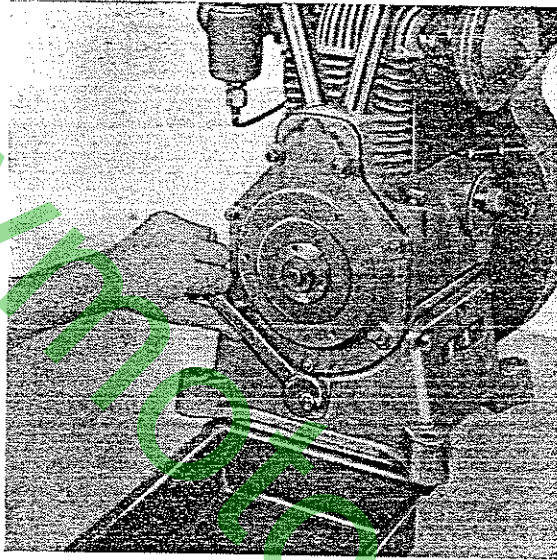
Desserrage de la vis sur la face arrière pour la vidange d'huile
